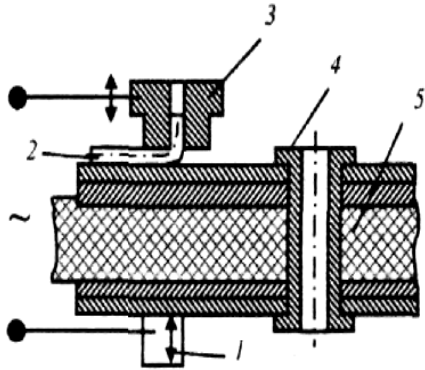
Схема сварки монтажных проводов: 1, 3 – электроды,
